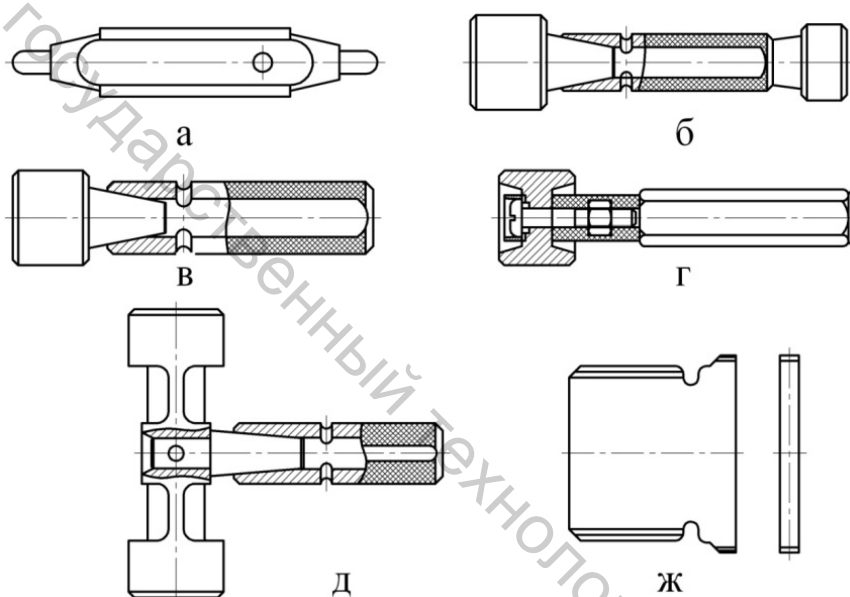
Схемы конструкций калибров-пробок:
